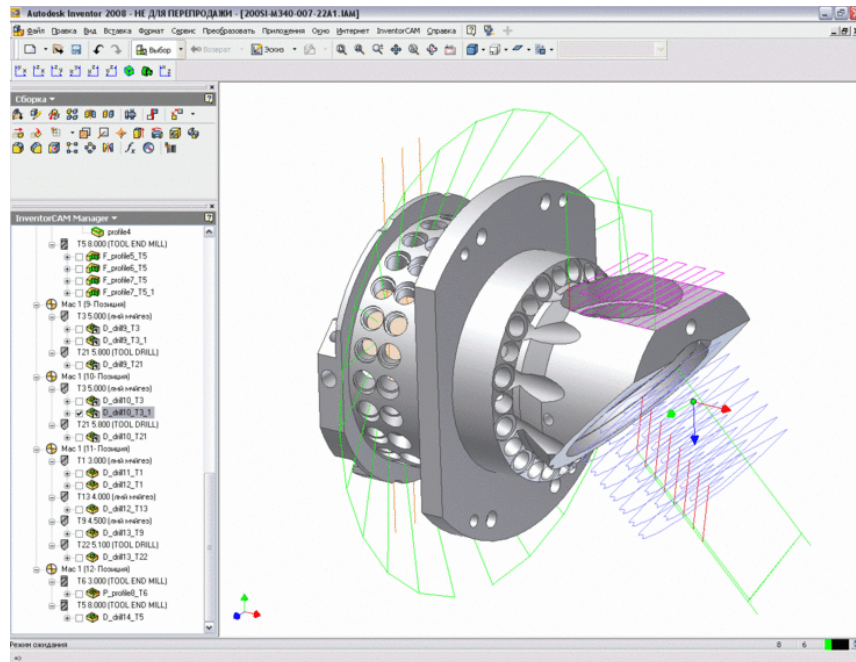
Позиційна 3D + 2D-фрезерна обробка
